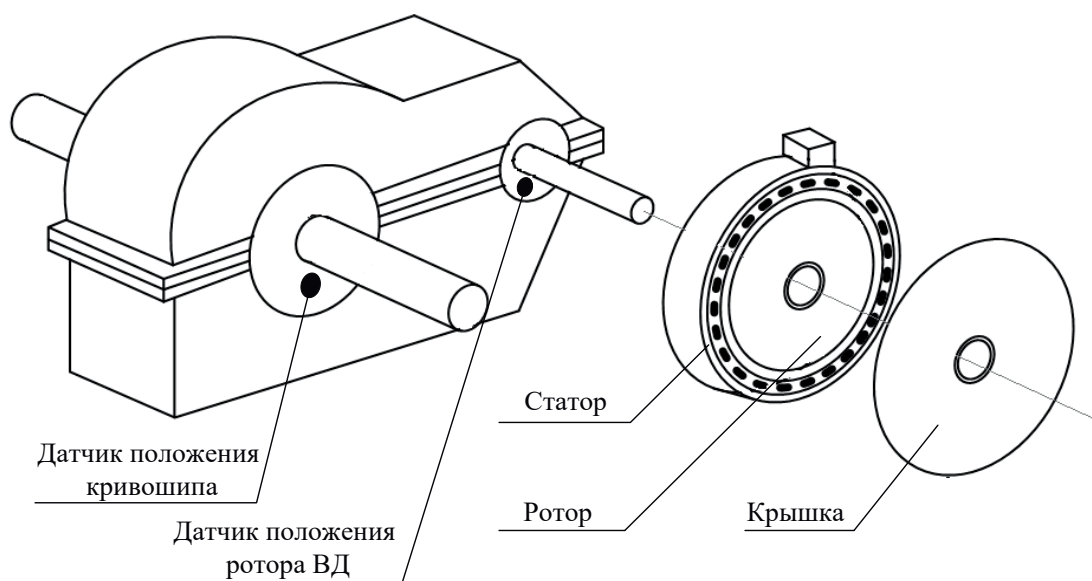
Вентильный двигатель для установки штангового глубинного насоса
